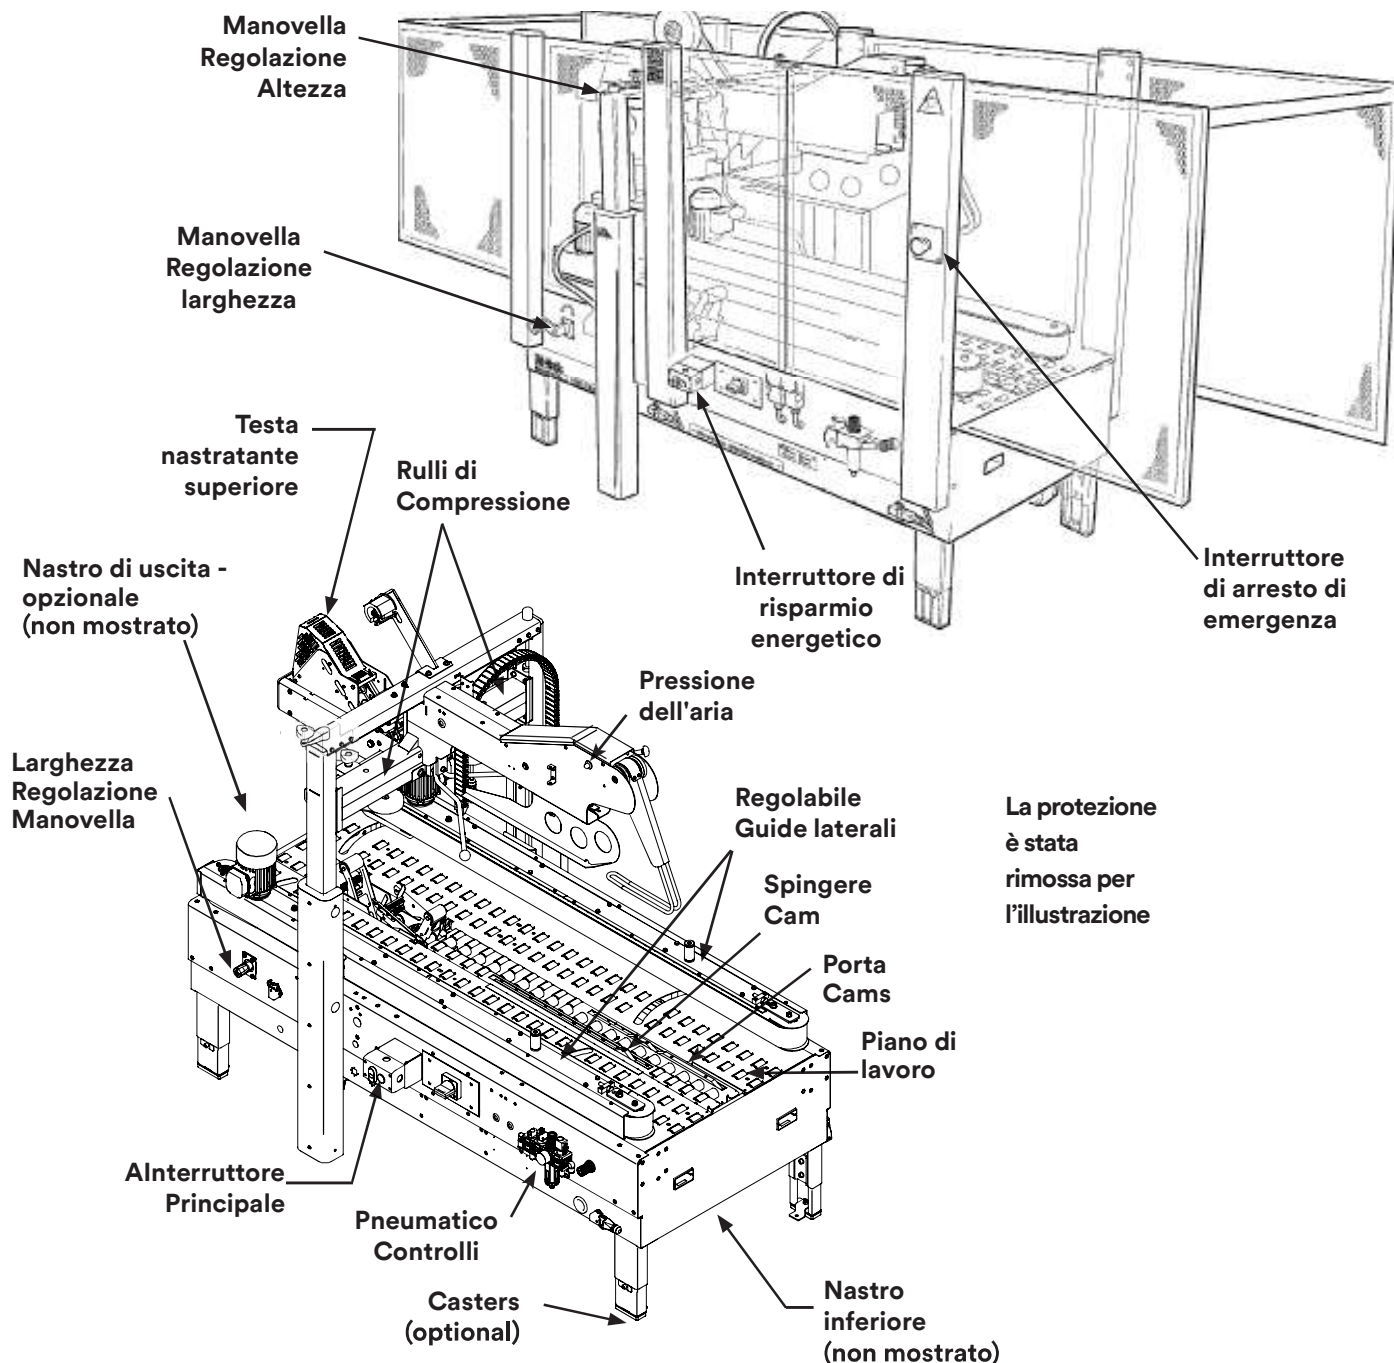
8000af-I/8000af3-I Componenti del sistema di sigillatura (Vista frontale sinistra)
